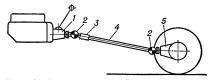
Схема карданной передачи автомобиля: 1 — коробка передач; 2 — кардан; 3 — скользящее шлицевое соединение; 4 — карданный вал; 5 — главная передача.
